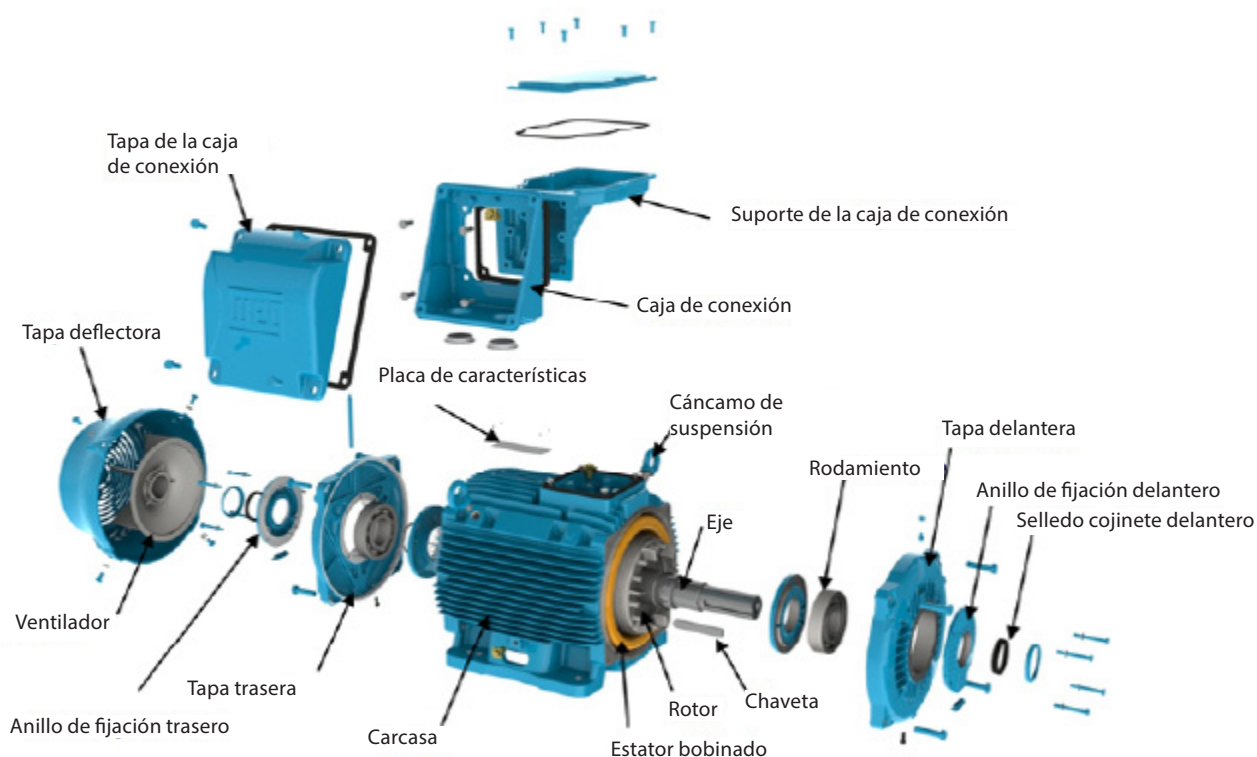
Vista en despiece de los componentes de un motor W22
